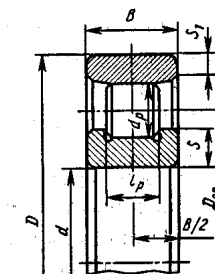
Подшипник роликовый радиальный с короткими цилиндрическими роликами
